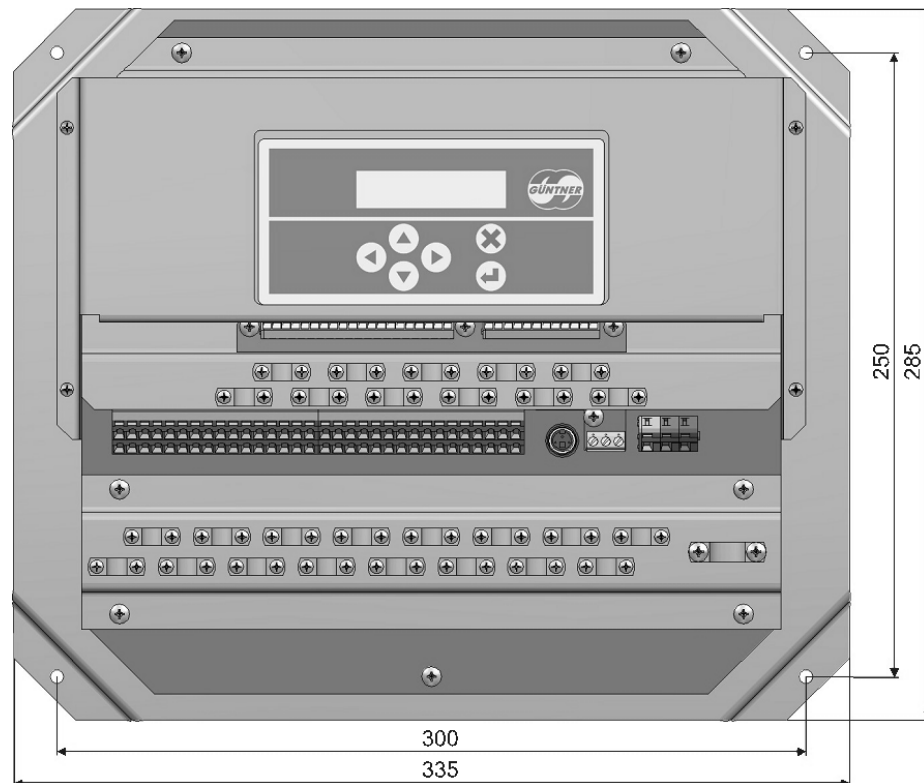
Dimensões de caixa GMM EC 16 (.1) UL
